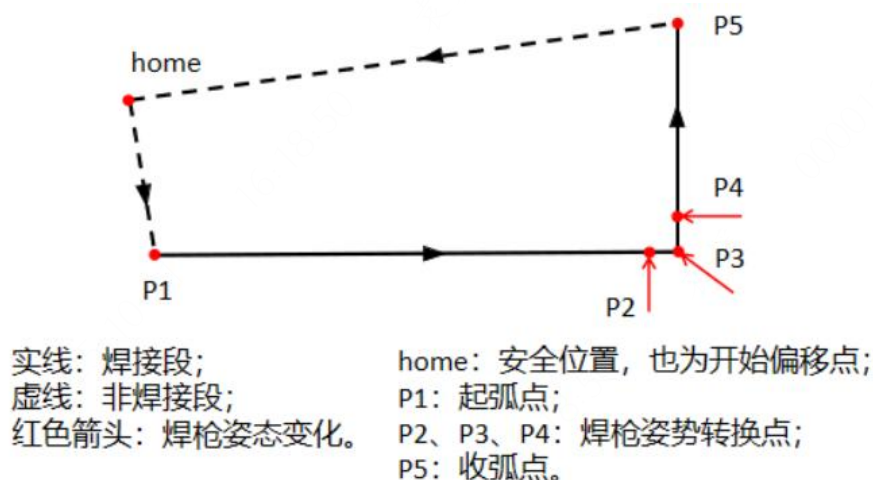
多道直线单一方向多层多道焊示意图
